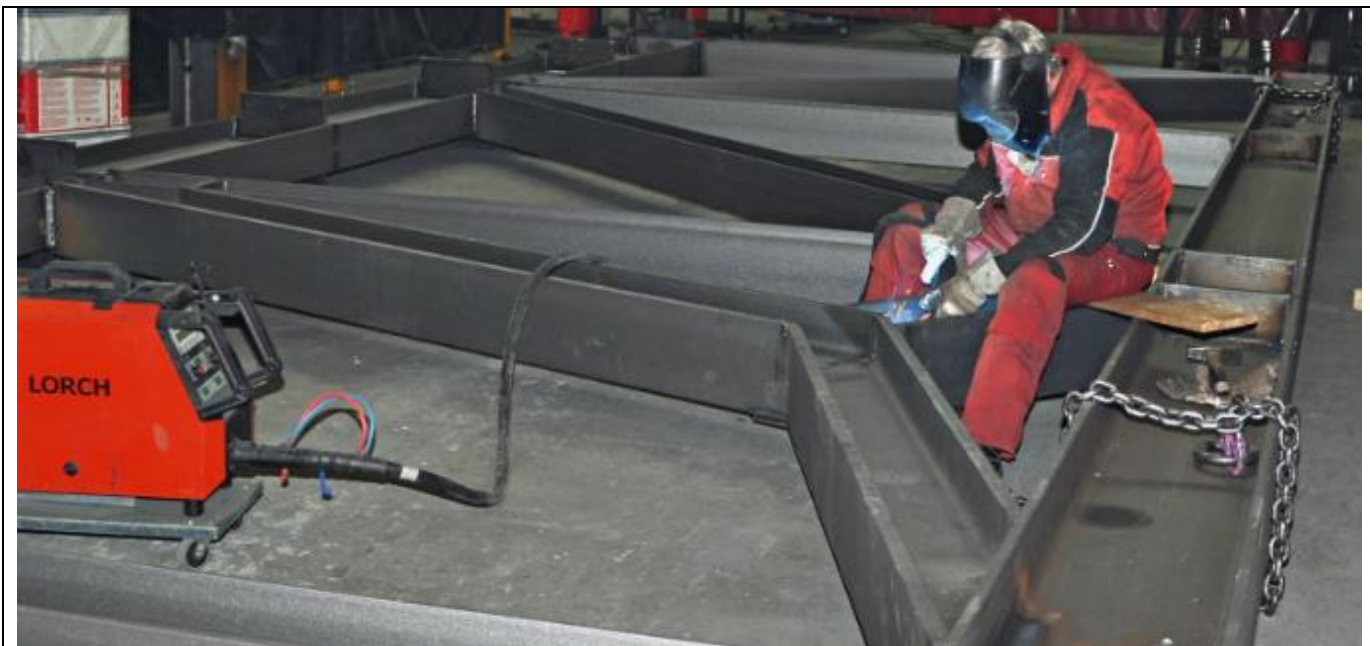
Profilträger werden zu Fachwerkverbindern verschweißt
